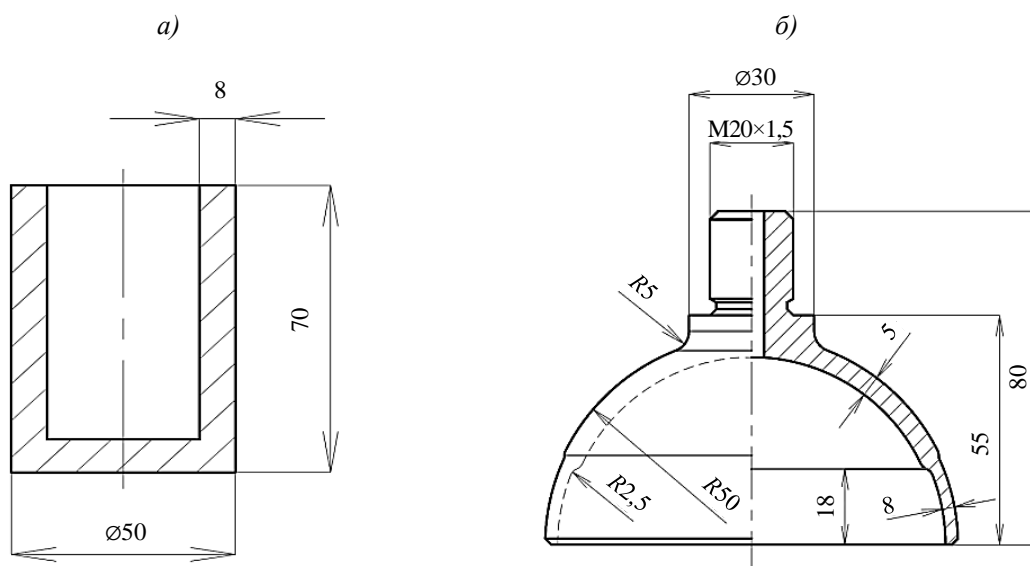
Отливки для испытаний на герметичность типа «полый цилиндр» (а) и «полусфера» (б)
